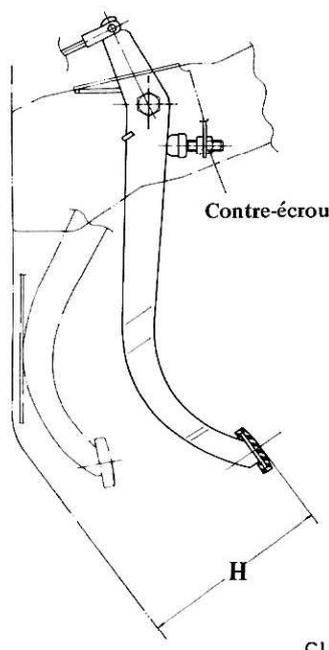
Réglage de la hauteur de pédale d'embrayage
